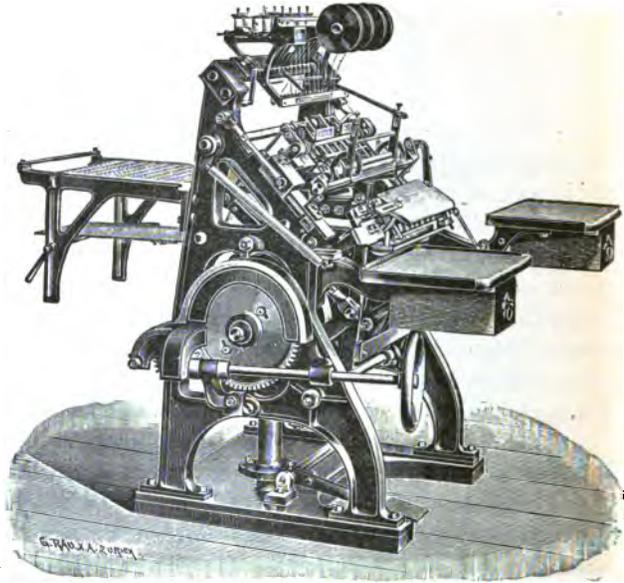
Machine à coudre ; reliures et emboîtages.
